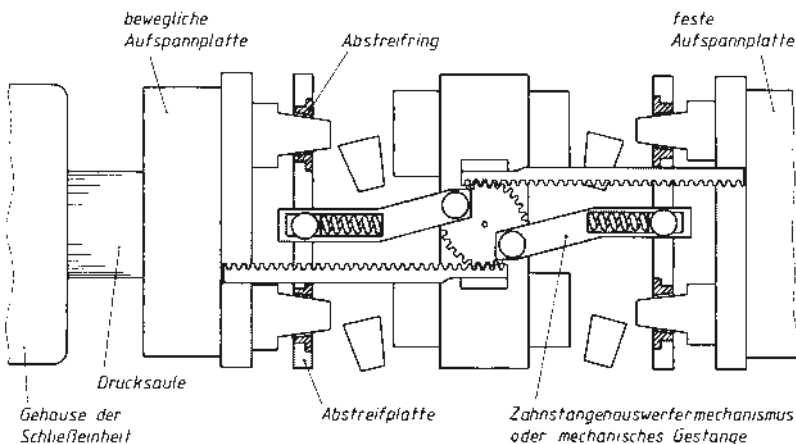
Zahnstangengetriebe zur Bewegung des Mittelsegments und der Auswerfer bei Etagenwerkzeugen [13.12]
